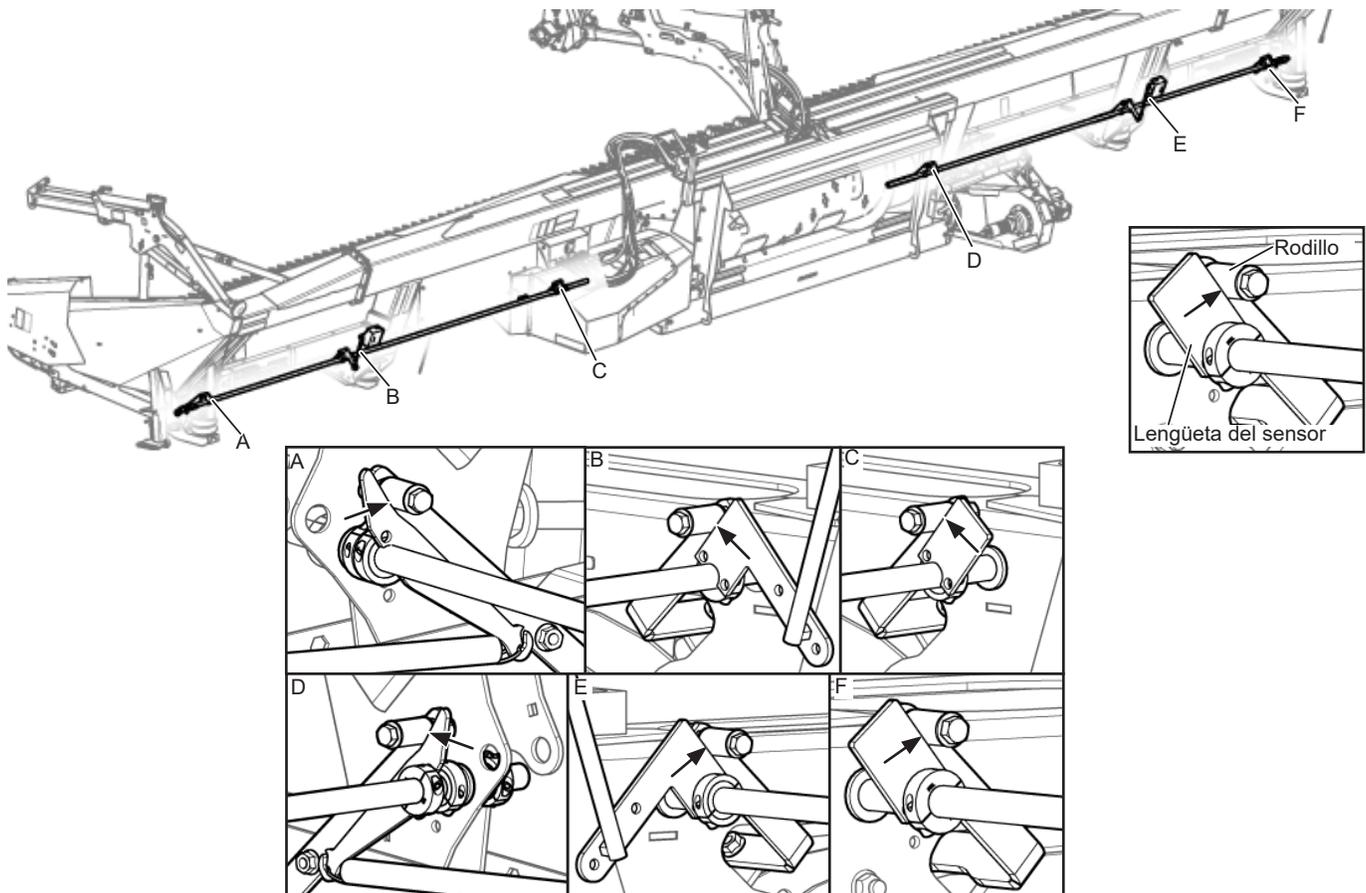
Posiciones de contacto del sensor FLEX HHC
